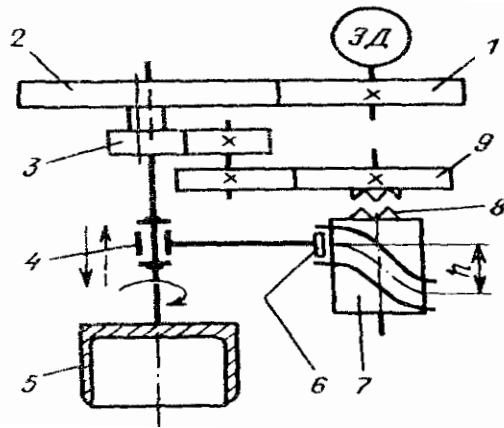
Механизм привода цилиндрического ножа:
